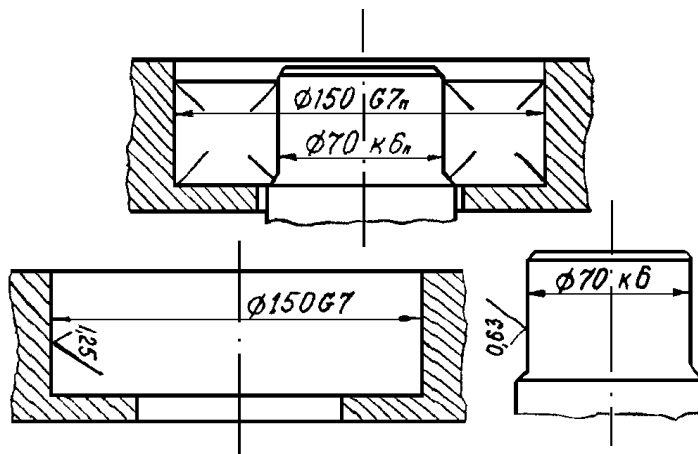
Обозначение посадок подшипников и полей допусков сопрягаемых с ними деталей
